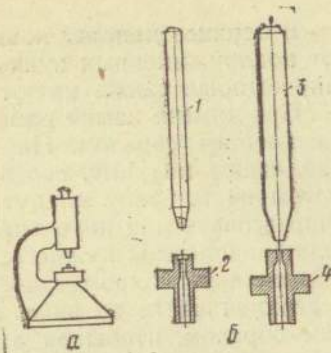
Потанс для выпрессовки и запрессовки оси баланса:
